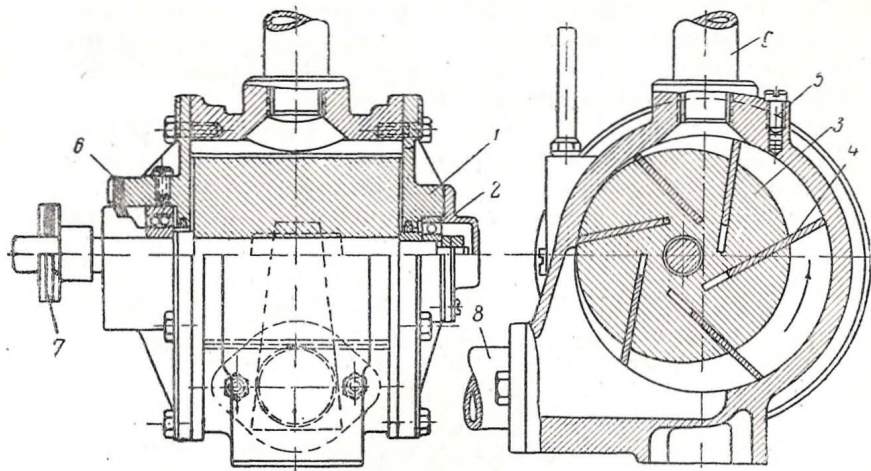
Схема воздуходувки „Мехмашстрой № 2“.
